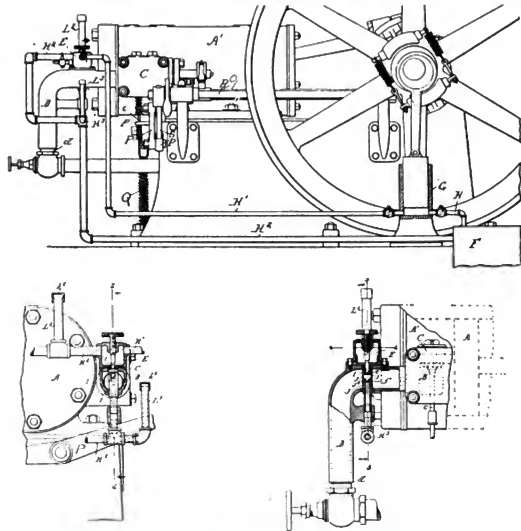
, 8 u. 9. Vorrichtung für Explosionsmotoren ohne Karburatoren.
